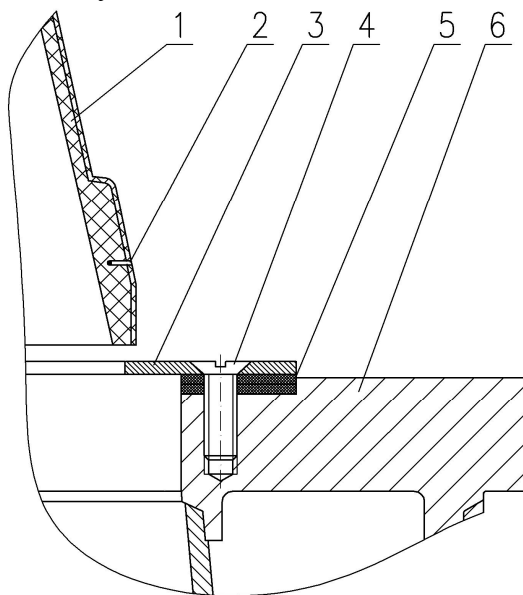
Модернизированная конструкция узла стыка среза соплового насадка со стендовым оборудованием: 1-насадок из УУКМ; 2-термопара; 3-кольцо; 4-винт; 5- паронитовые кольца; 6-регулирующее кольцо ГДТ
